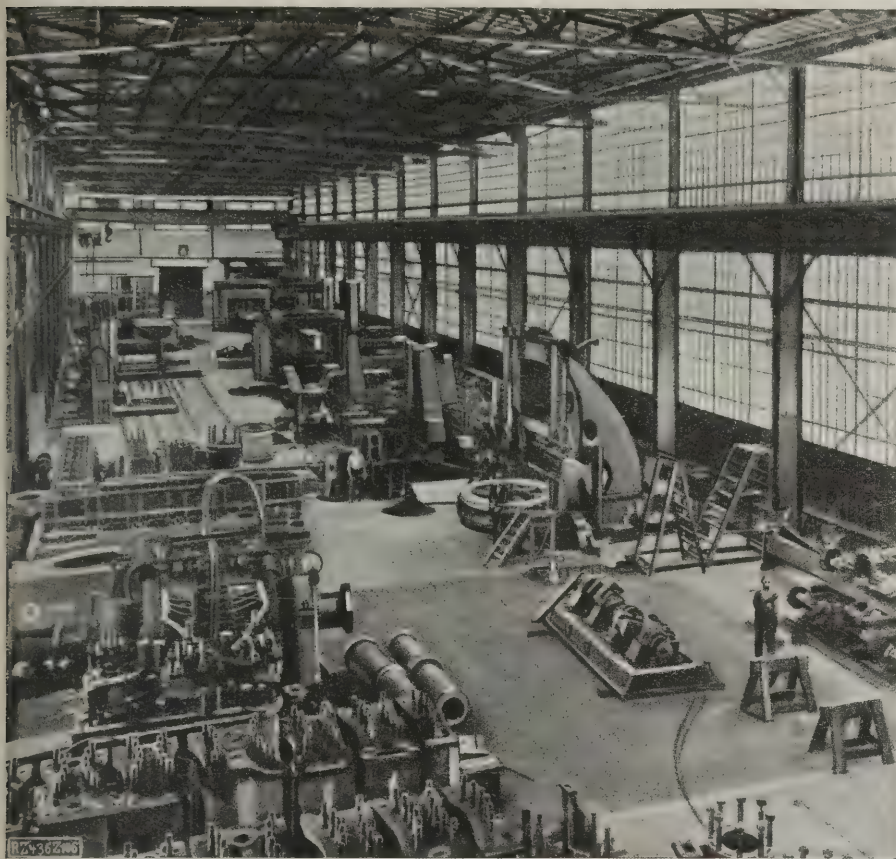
Bearbeitungswerkstatt für Dieselmotoren.
